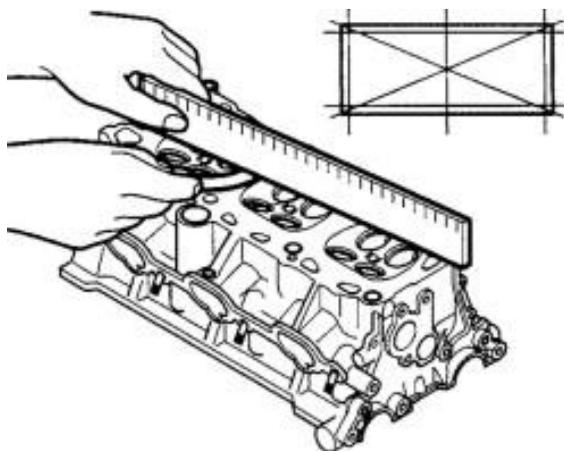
Проверка неплоскостности прилегающей поверхности головки блока цилиндров
